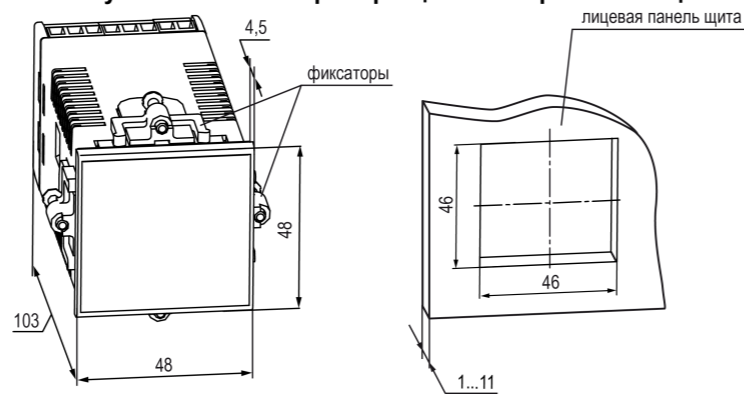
Габаритные размеры корпуса Щ5 и монтажного отверстия в щите
